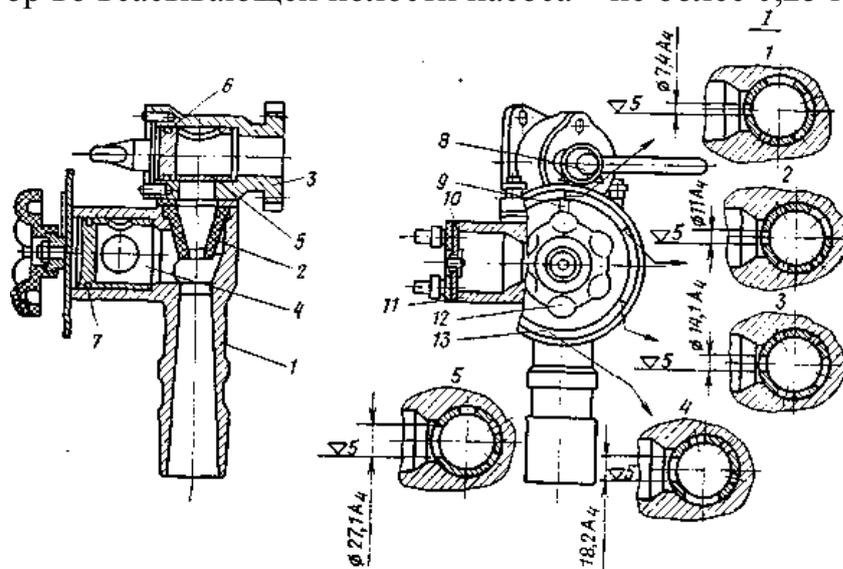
Пеносмеситель ПС–5: 1 – корпус; 2 – дозатор; 3 – сопло; 4 – пробка крана; 5 – корпус крана; 5, 7 – уплотнительные кольца; 8 – ручка; 9 – стрелка; 10 – обратный клапан; 11 – крышка клапана; 12 – маховичок; 13 – шкала; I – положения дозатора
